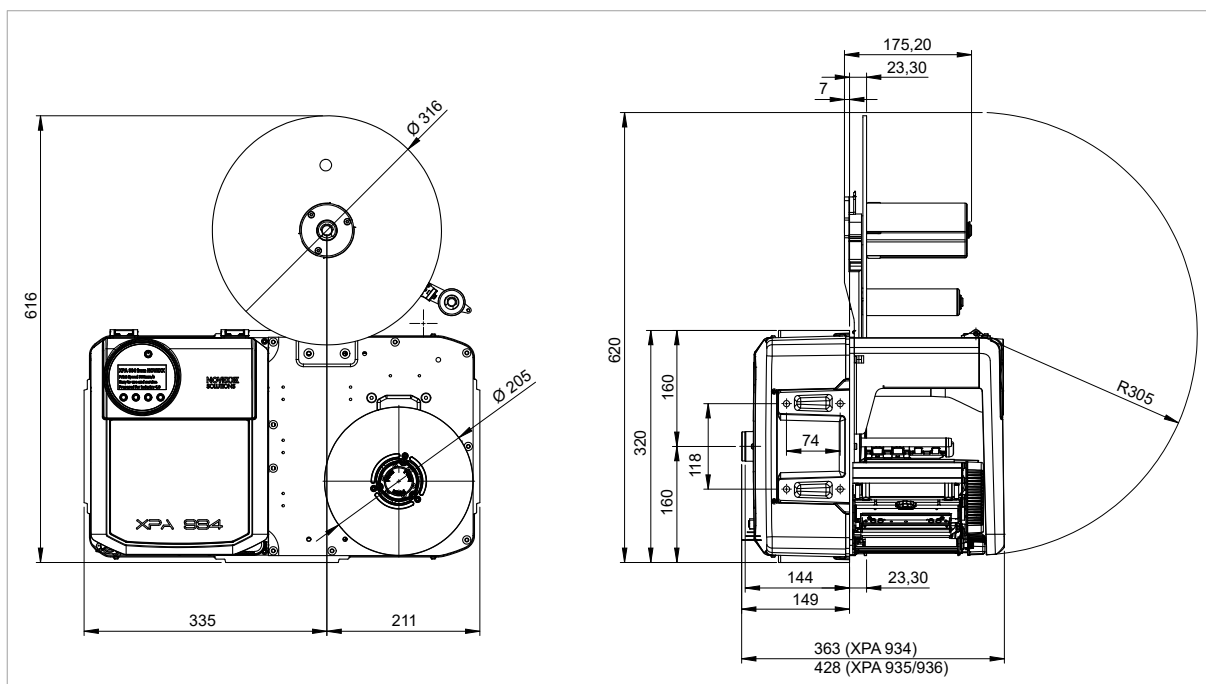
Dimensiones del XPA 934 LH con desenrollador Compact.
